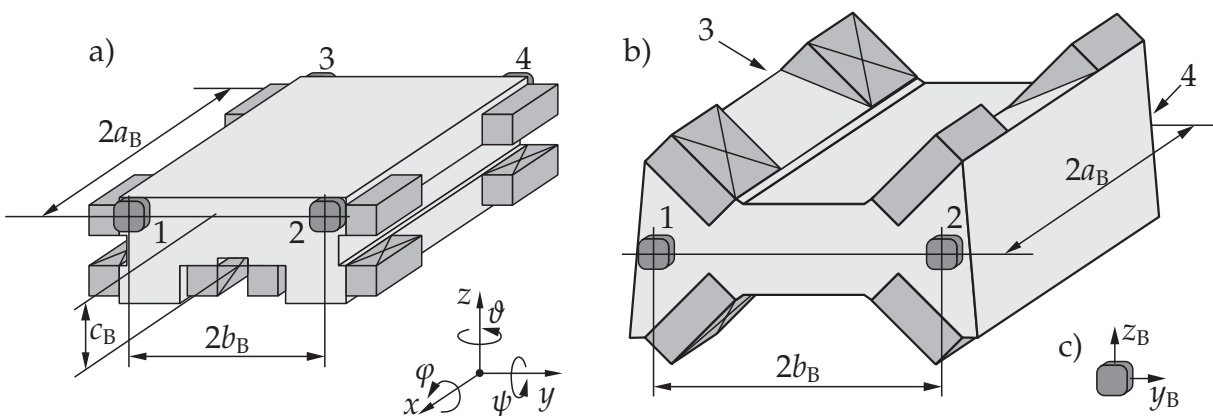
Anordnung der Beschleunigungssensoren: a) Prototyp-Führung; b) Maschinenachse; c) Koordinaten eines Sensors
